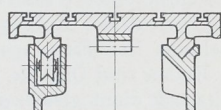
Schlittenführung an Werkzeugmaschinen.
